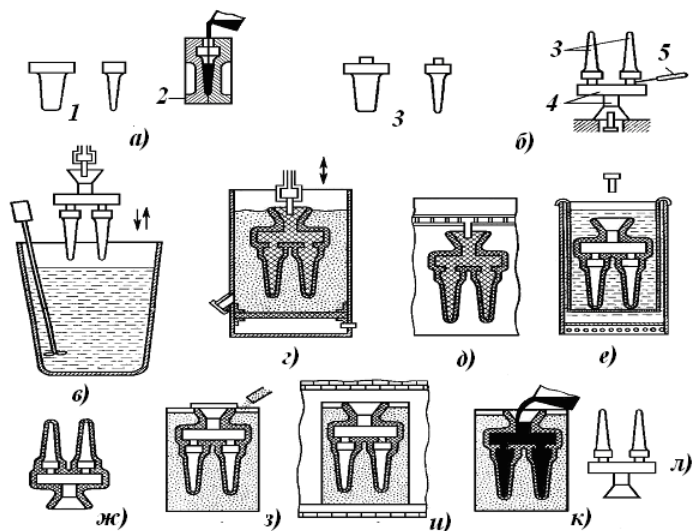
Схема процесса изготовления отливок по выплавляемым моделям
